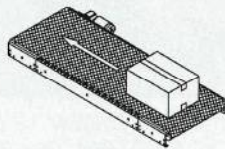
Rollen-Bandbettung, horizontale Beförderung
